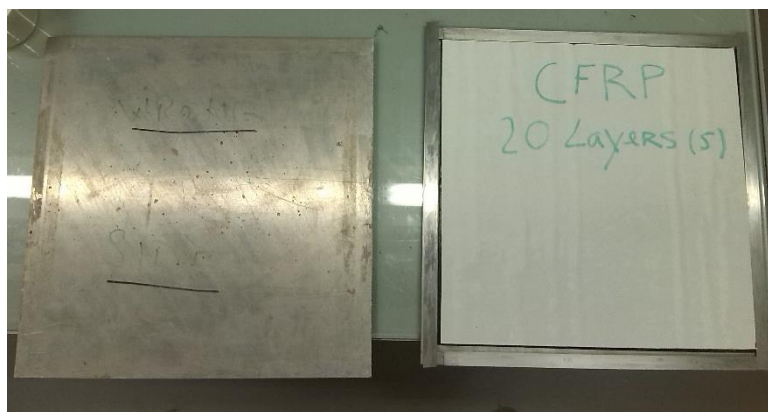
Posicionamento da placa de carbono-epóxico no molde
